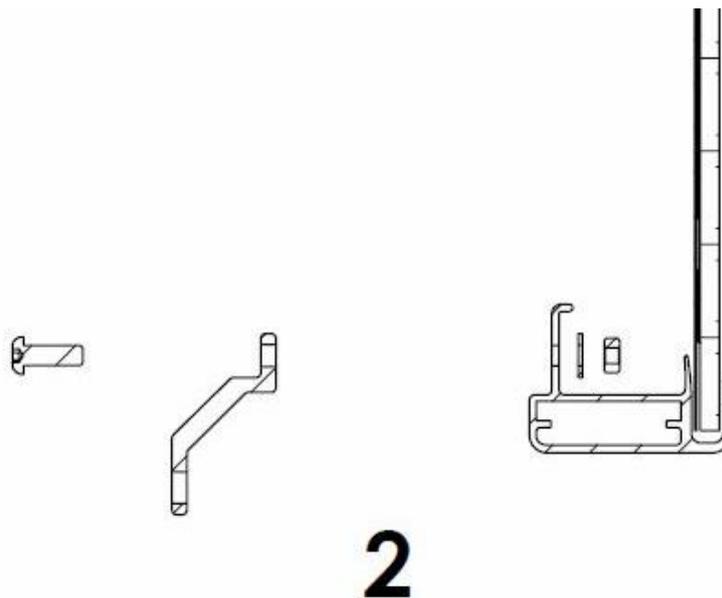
Detailansicht (Schnitt) zur Montage von zwei Wandhalterung Laschen
